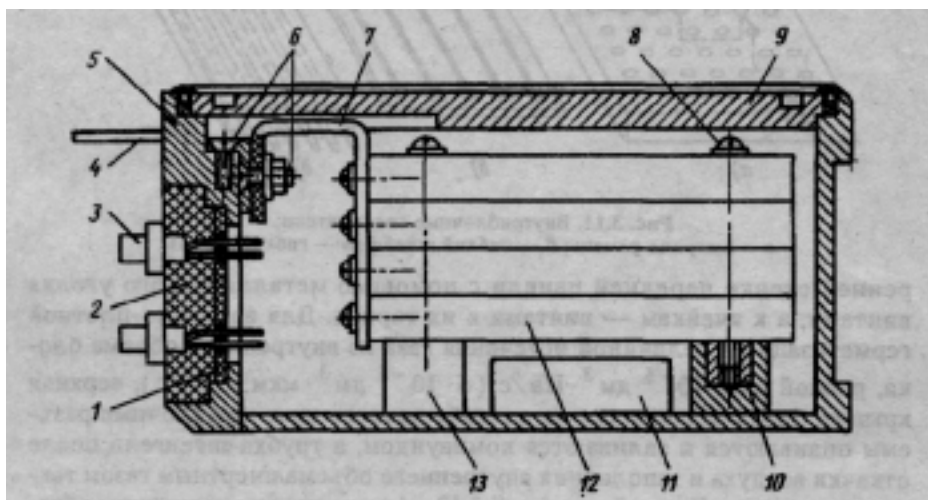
Конструкция блока книжной компоновки IV поколения:
